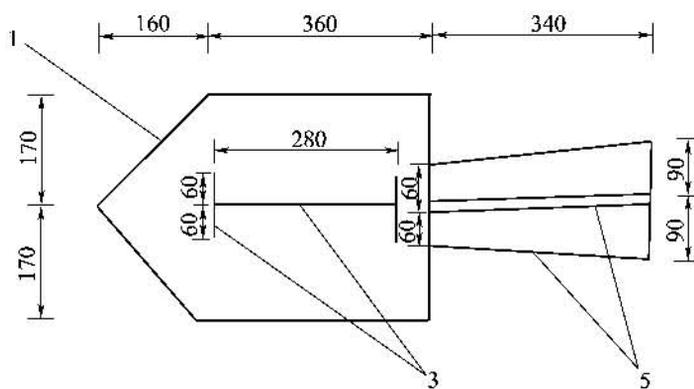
底质打印探测器正面图(尺寸单位:mm)
